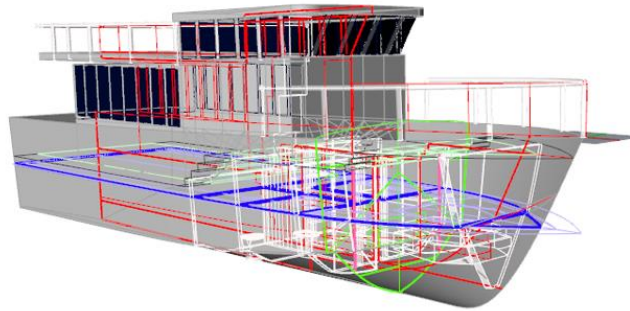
Alt güverte plan kesit alternatif 2 karşılaştırması
